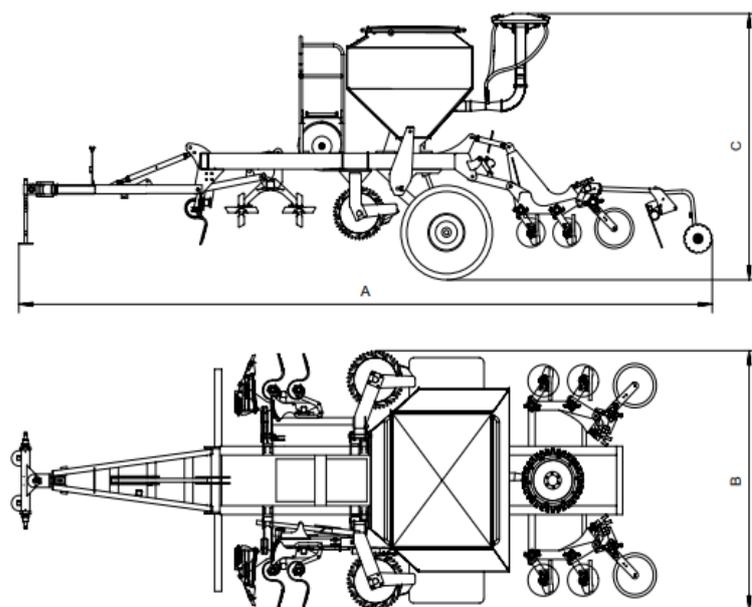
Схема агрегата MegaSeedc дисково-ножевой бороной
